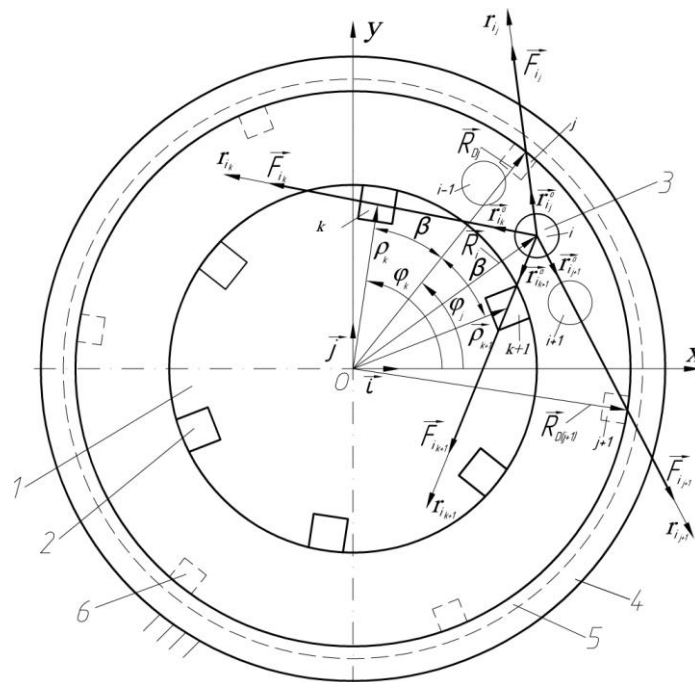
Схема руху деформувальної кулі від магнітної системи інструмента до поверхні деталі, яку зміцнюють; 1 – магнітна система інструмента; 2 – джерела магнітного поля, надають деформувальній кулі робочого руху; 3 – деформувальна куля; 4 – оброблювана деталь; 5 – поверхневий шар деталі, який намагнічується; 6 – умовне зображення джерел магнітного поля інструмента, що забезпечують намагнічування поверхневого шару деталі
